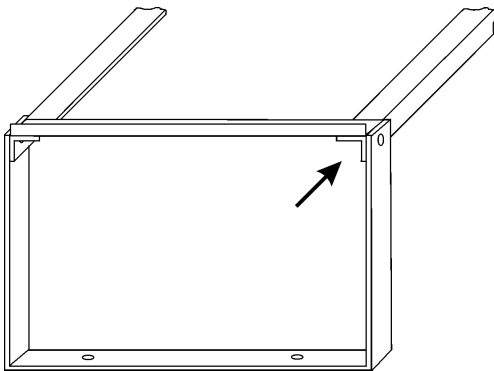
Befestigungsrichtung der Wandhalterung bei Standard-Montage, Ansicht von oben
